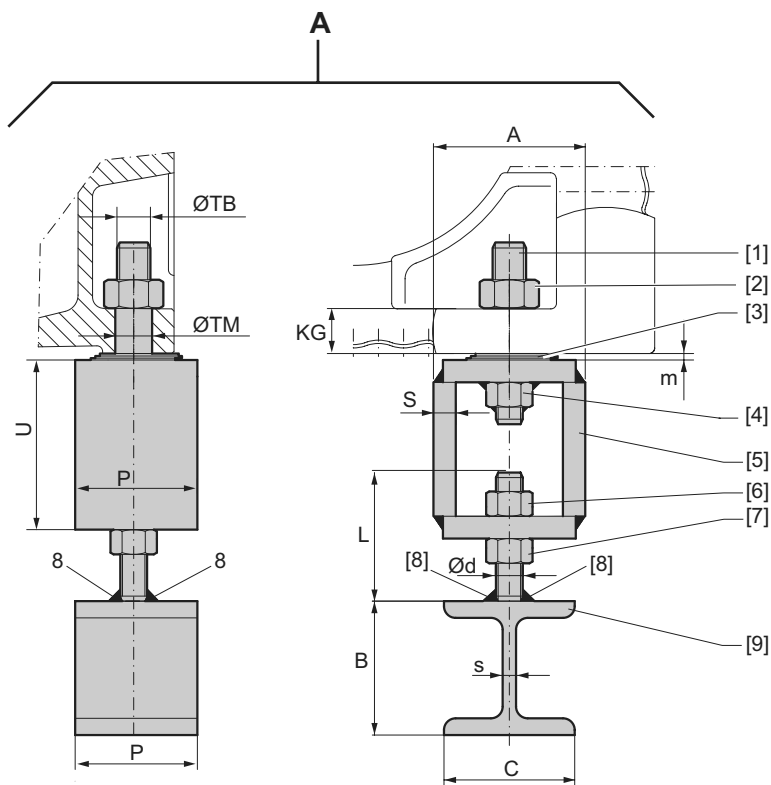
Refuerzo de la base de cemento (Pos. "A")
